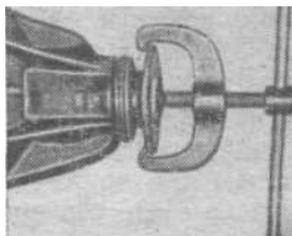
Съемник фланца вала ведущей шестерни редуктора
